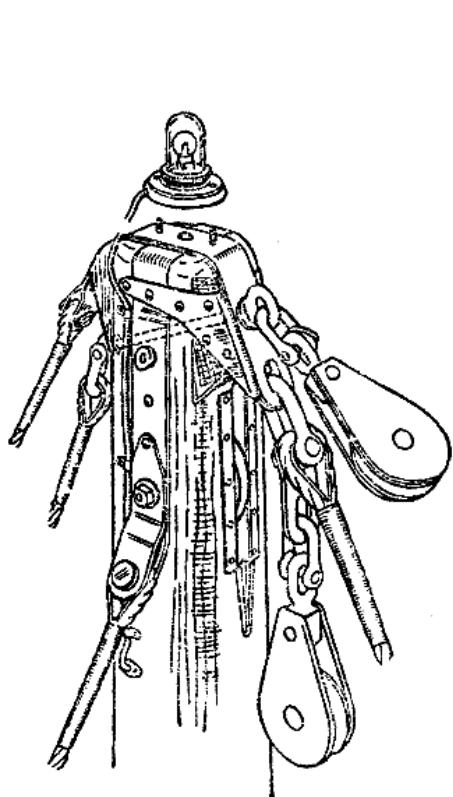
Английская оковка топа мачты, при изготовлении которой широко использованы стандартные стальные детали (по Хэману)
